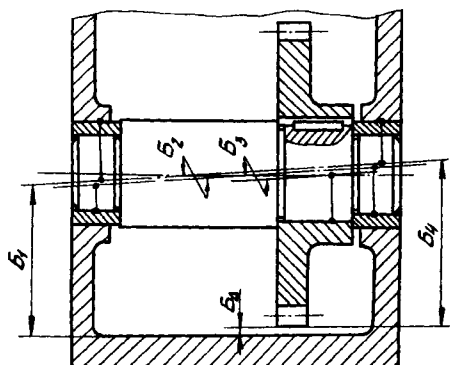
Схема размерной цепи, определяющей возможность установки зубчатого колеса в редукторе при сборке
